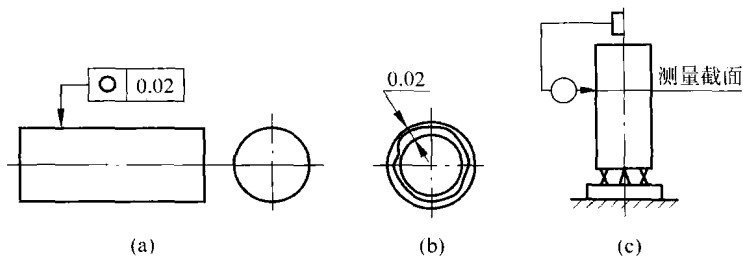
圆度公差的标注、公差带及测量方法
